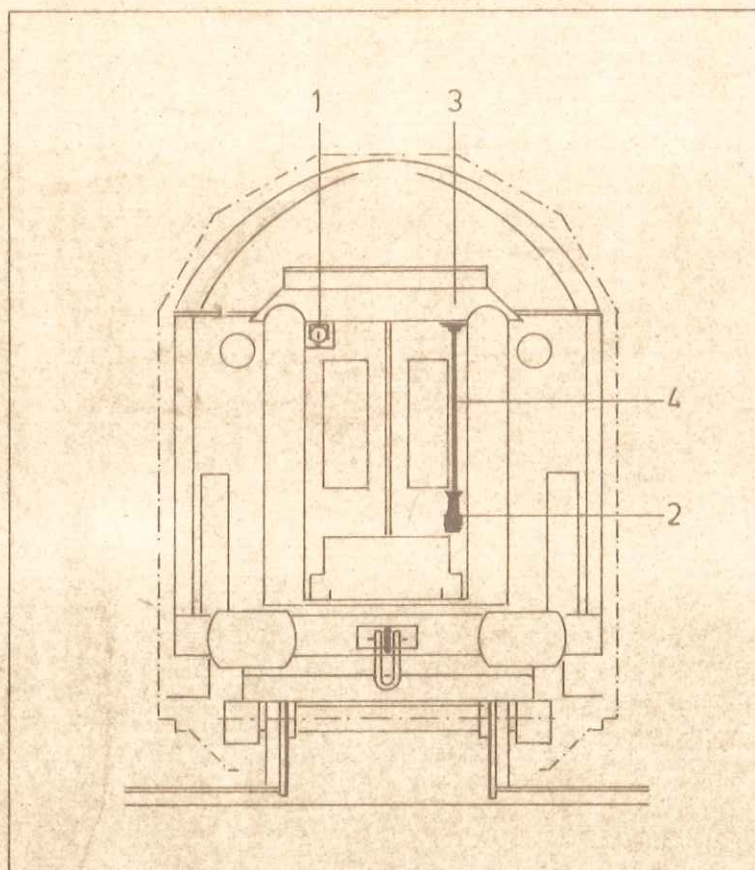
Штепсельная розетка и кабельная штепсельная вилка 13-полюсная на передней стене вагона
